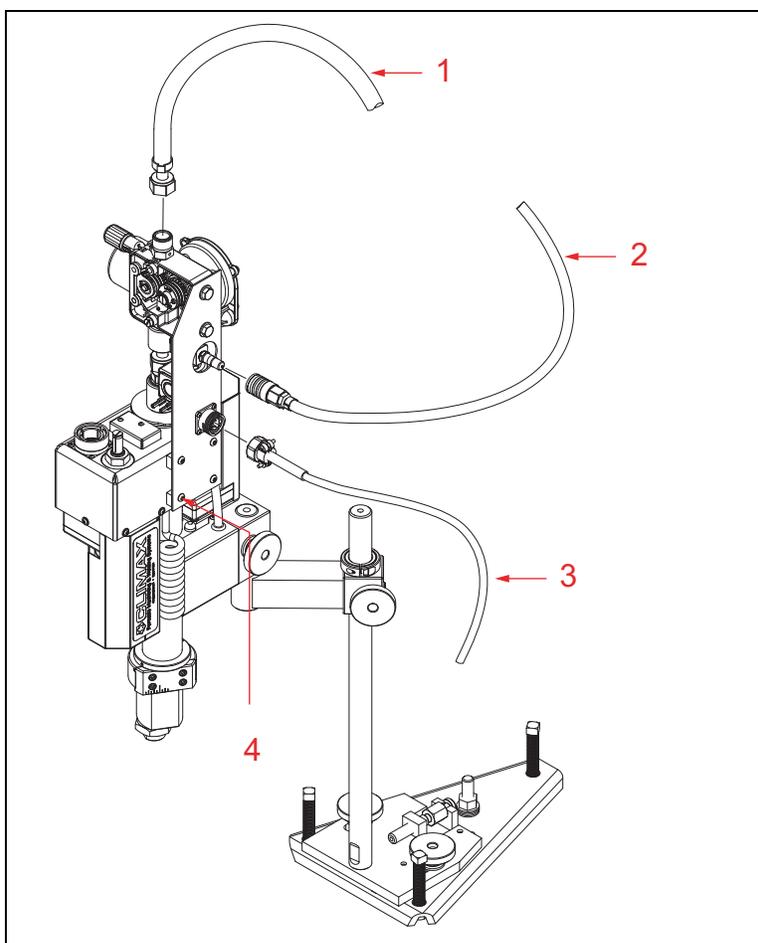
Возвратно-поступательный механизм подачи проволоки
